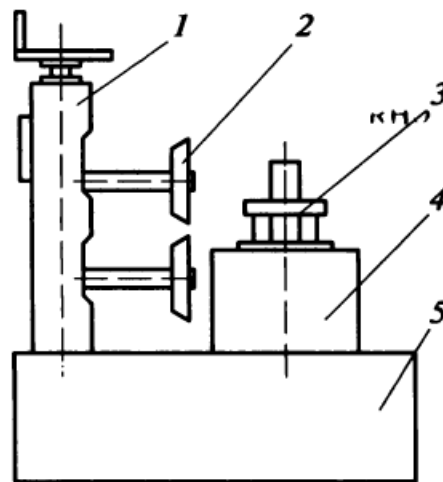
Схема станда 1102 для демонтажных работ шин: 1 — стойка с винтом; 2 — нажимные ролики; 3 — сменная ступица; 4 — рабочий стол; 5 — каркас
